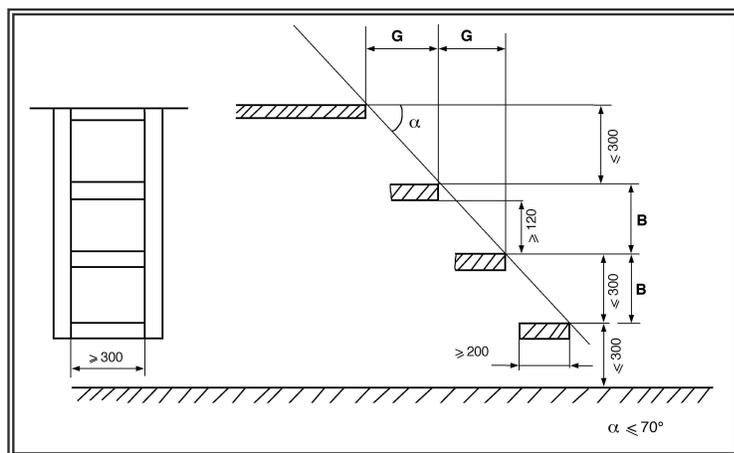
Dimensioni dei mezzi d'accesso alla zona di carico
